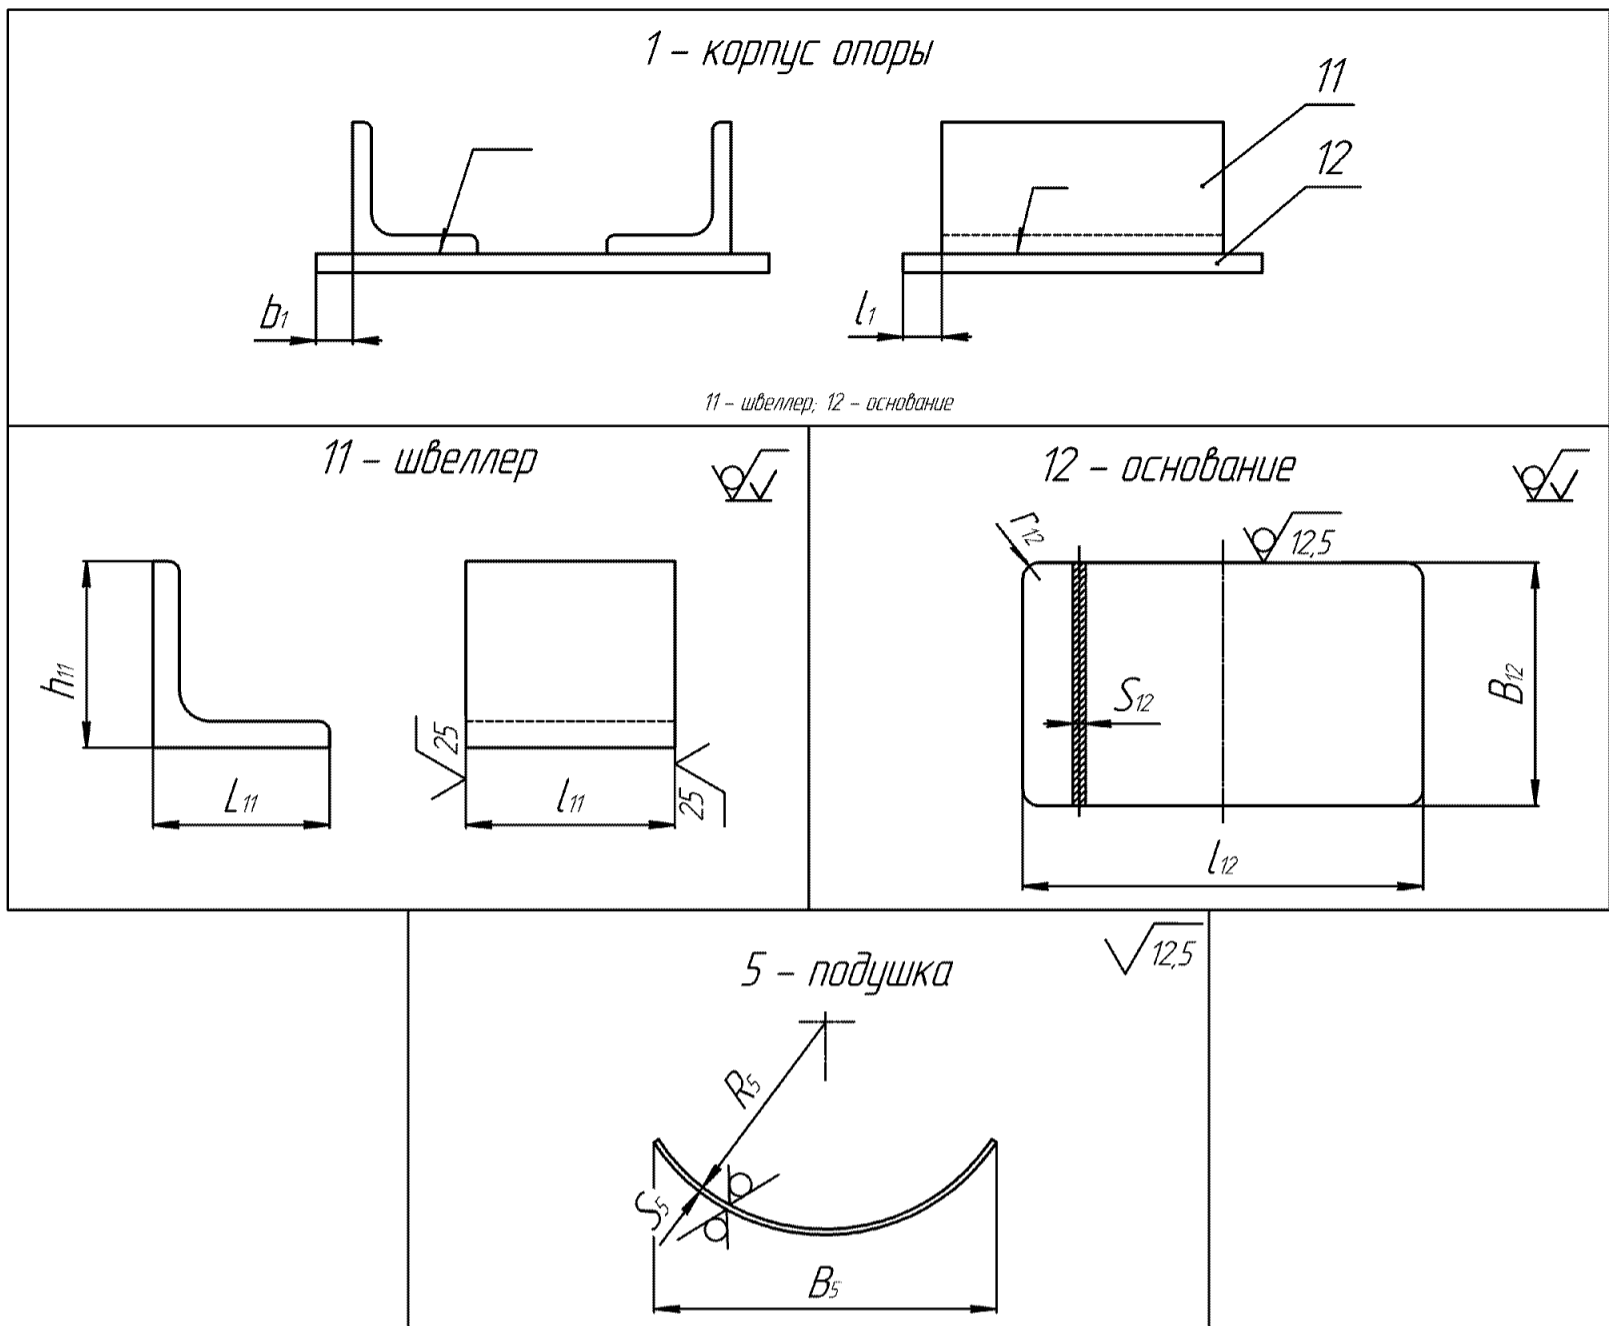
Детали изделий 02-XXXX-S-1C-XX-C и
